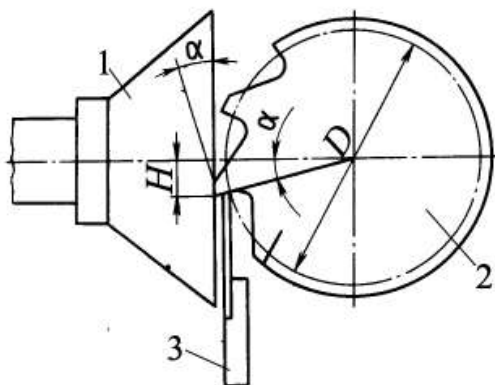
Схема заточування циліндричної фрези на універсально-заточувальному верстаті
